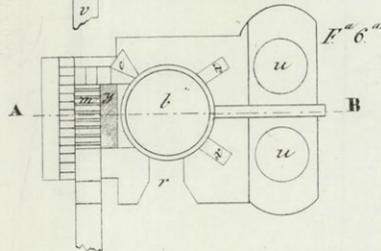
<sup>a</sup> Seccion horizontal a la altura del puente.
